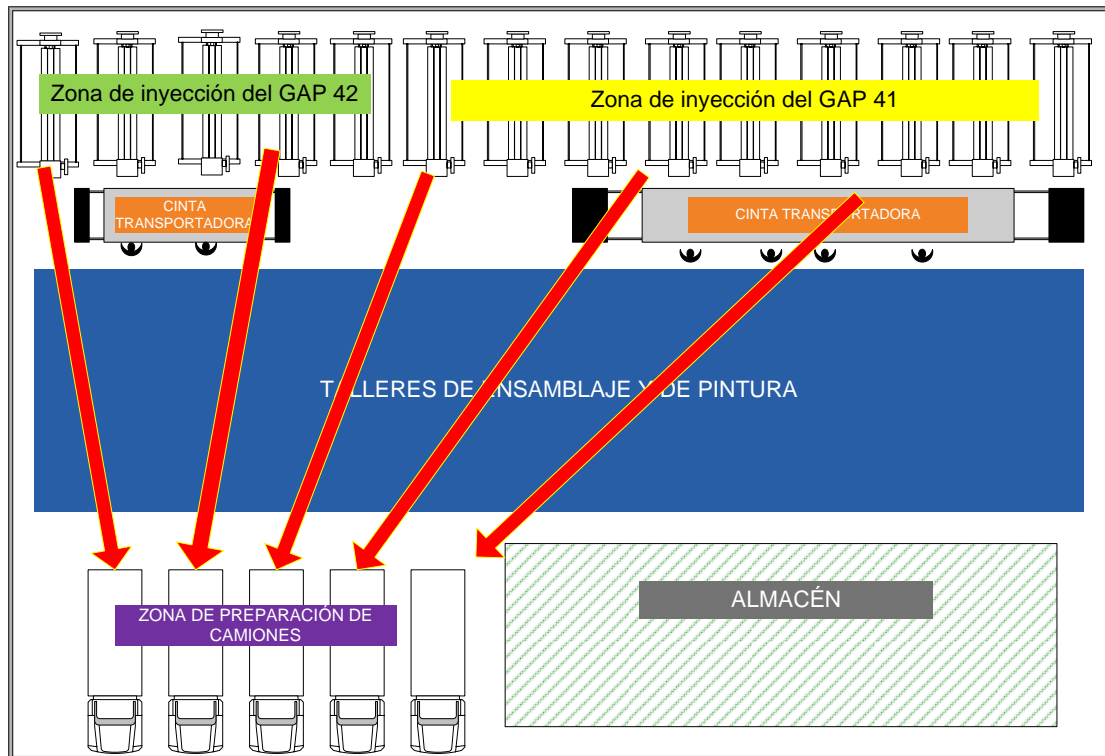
Plano y flujo de trabajo en la planta de Fradley
